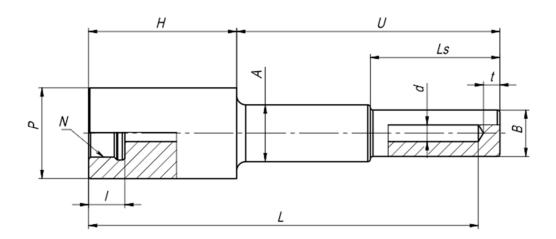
Гильза под приварку через адаптер (Socket Weld), цельноточёная, ступенчатая, под неподвижный штуцер.
